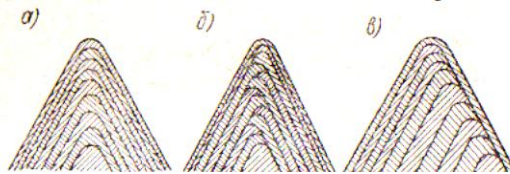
Способы углубления резца при образовании винтовых канавок резьбы
